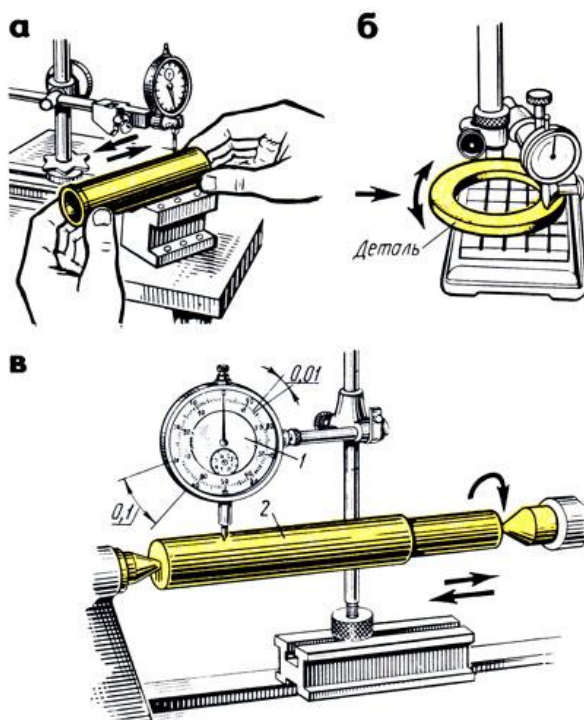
Приемы проверки индикатором: а, б - перемещением деталей, в - в центрах; 1 - индикатор, 2 - деталь
